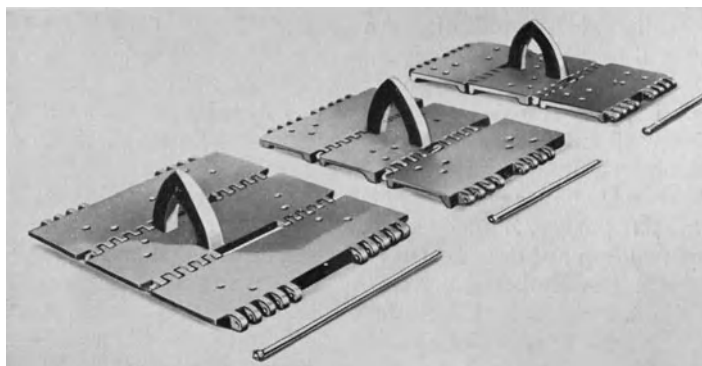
Raupenplatten für den Rad-Raupen-Universalbagger.
